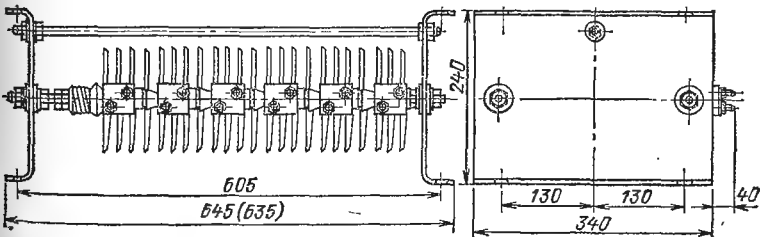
Размеры ящика резисторов стандартного ЯС100 или ЯС101 и кранового типа Н (размер 645 — стандартного ящика, 635 — ящика типа Н; все остальные размеры одинаковы).
